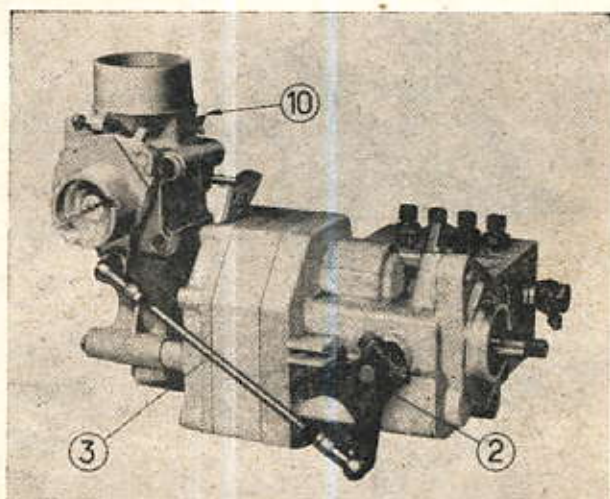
Vue d'ensemble de la pompe d'injection.
